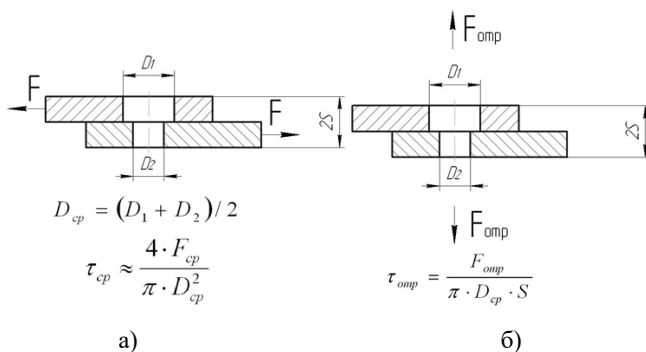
Схема испытания сварной точки: а — на срез, б — на отрыв
